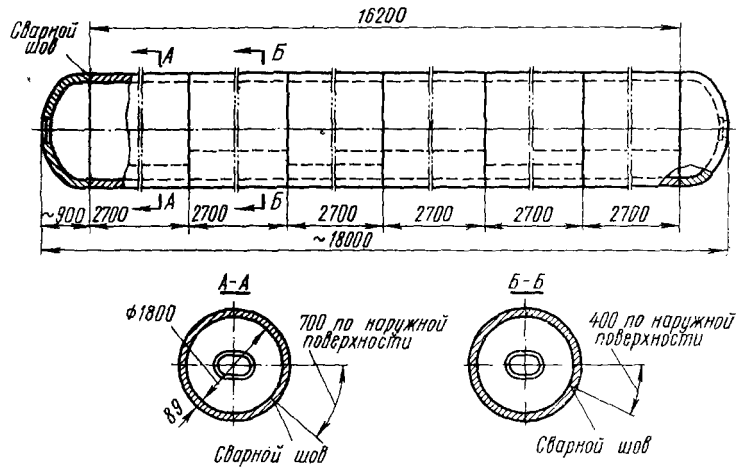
Общий вид сварного барабана котла ТП-80
